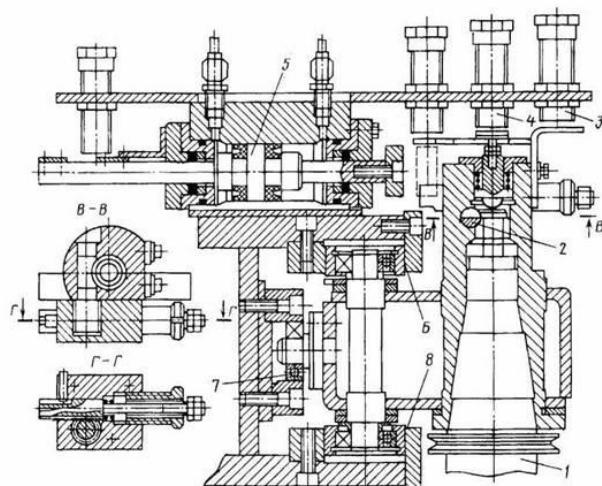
Инструментальный магазин в позиции смены инструмента
